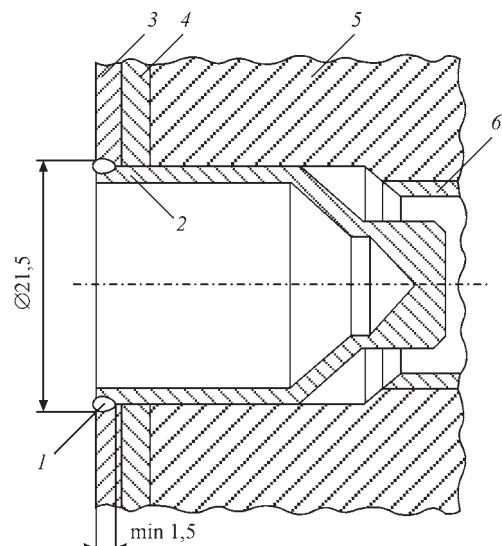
Схема вварювання заглушки: 1 – шов; 2 – заглушка; 3 – перший шар наплавлення; 4 – другий шар наплавлення; 5 – стінка ПГ; 6 – ТОТ
